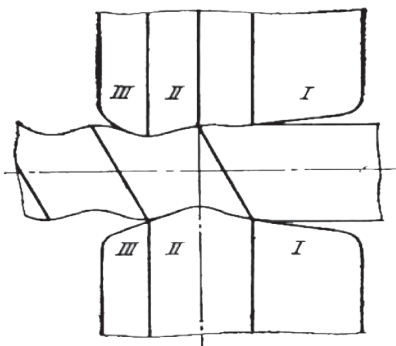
Калибровка прокатного инструмента и схема получения профиля на трубной заготовке
